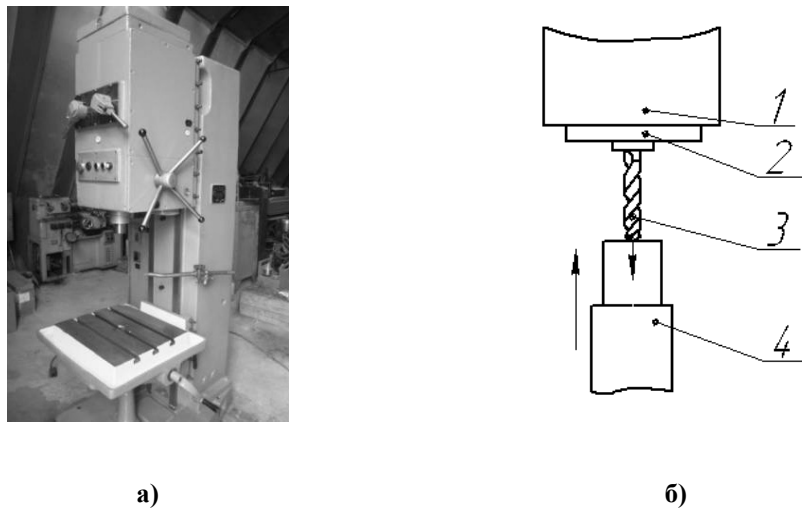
Дослідна установка: а – вигляд загальний; б – конструктивна схема: 1 – верстат; 2 – шпиндель; 3 – свердло; 4 – заготовка
